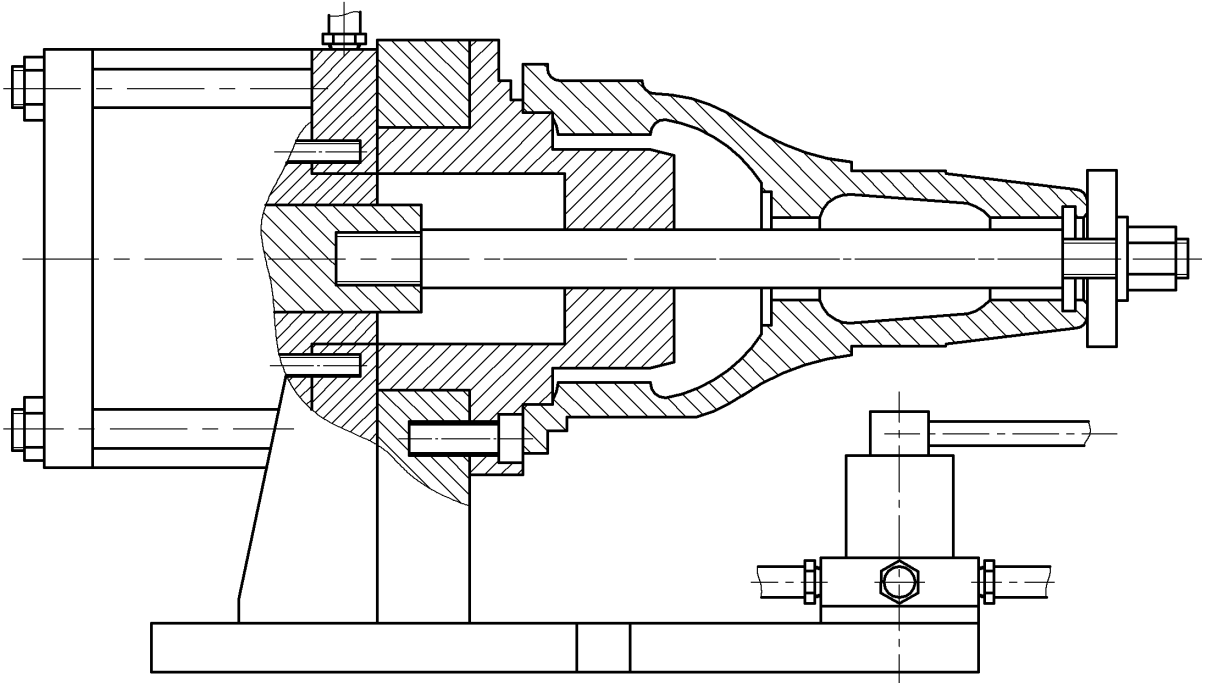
Загальний вигляд фрезерного пристрою для оброблення площадок розмірами  $65,25H12$  і  $73,25H12$
